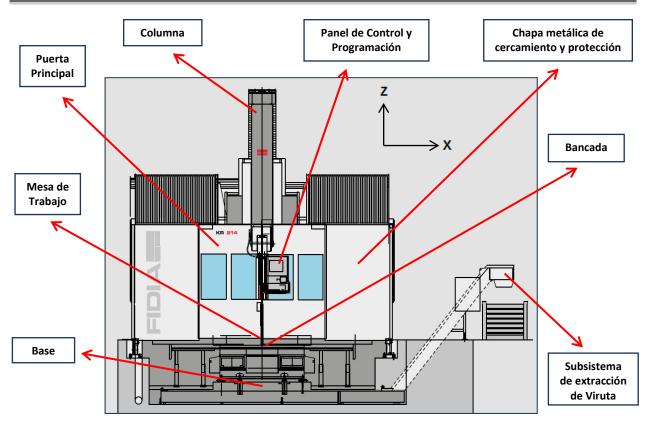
Partes de un Centro de Mecanizado: vista frontal
